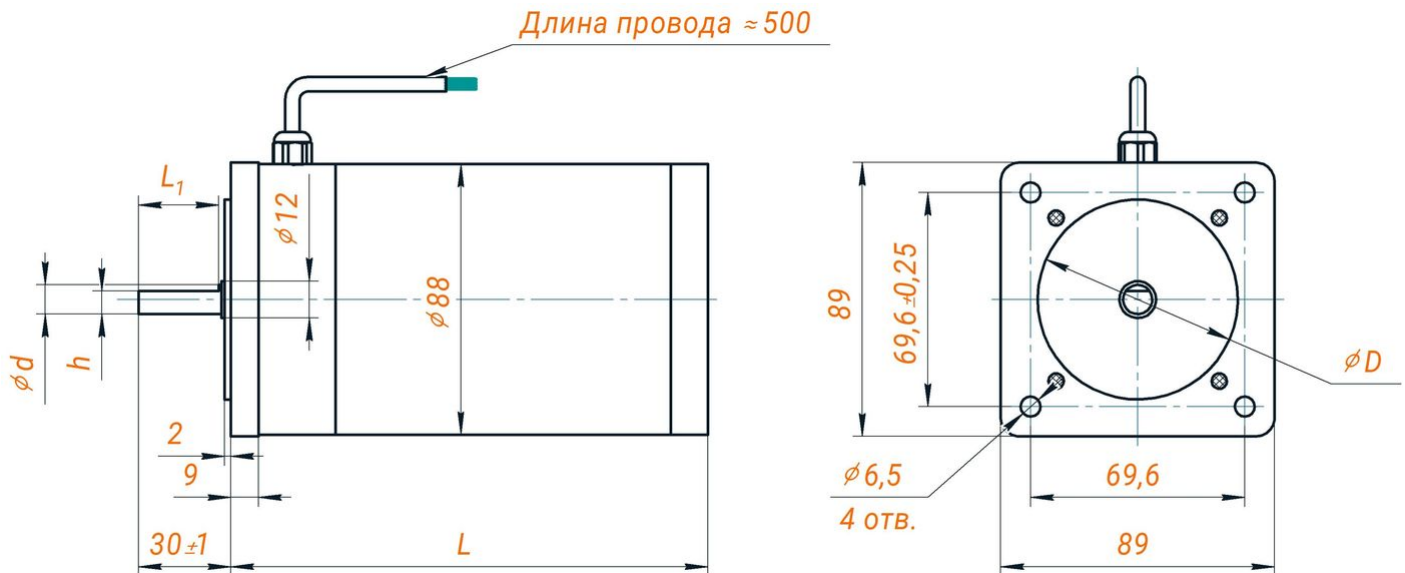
Габаритные размеры шаговых двигателей с IP68 серии 86
